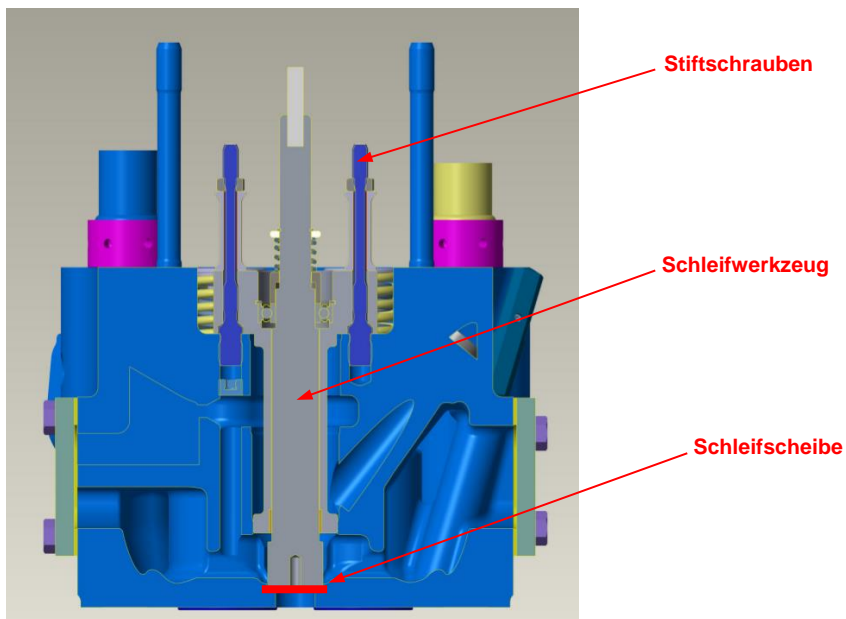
Montieren des Schleifwerkzeugs im Zylinderkopf
